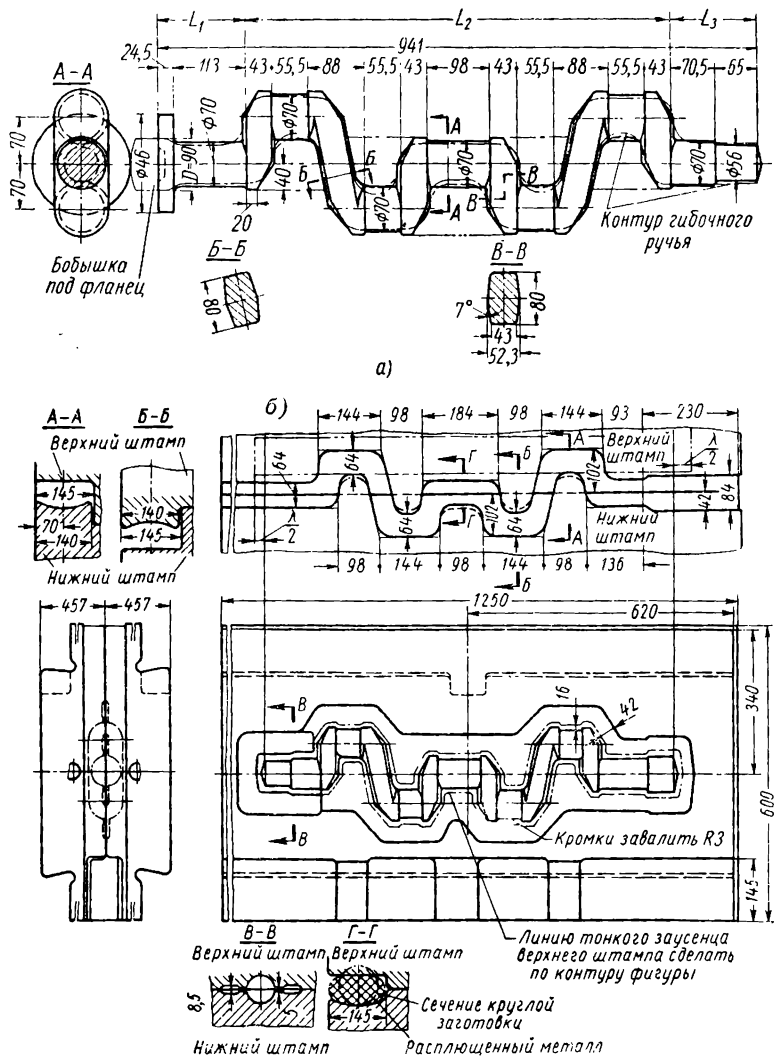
Штамповка коленчатого вала: а — поковка; б — молотовый штамп
